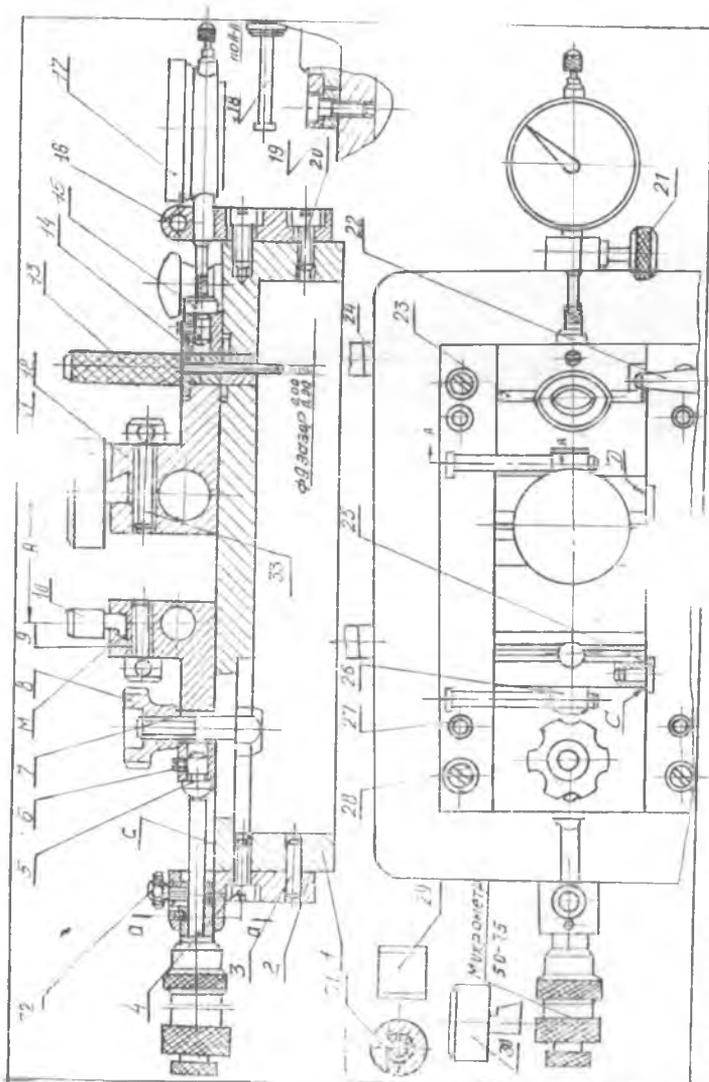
Прибор для измерения межцентровых расстояний: 1 — плита; 2, 16 — стойка; 3, 23, 27 — штифты; 4, 20, 21, 26, 28, 33 — винты; 5, 15, 25, 31 — упоры; 6 — стопор; 7 — болт; 8 — гайка; 9, 12 — полушны; 10, 11 — пальцы; 13 — штырь; 14 — втулка; 17 — индикатор; 18, 22, 24 — ручки; 19 — планка направляющая; 29 — эталон; 30 — установочный калибр; 31 — сегмент; 32 — стопорный винт
